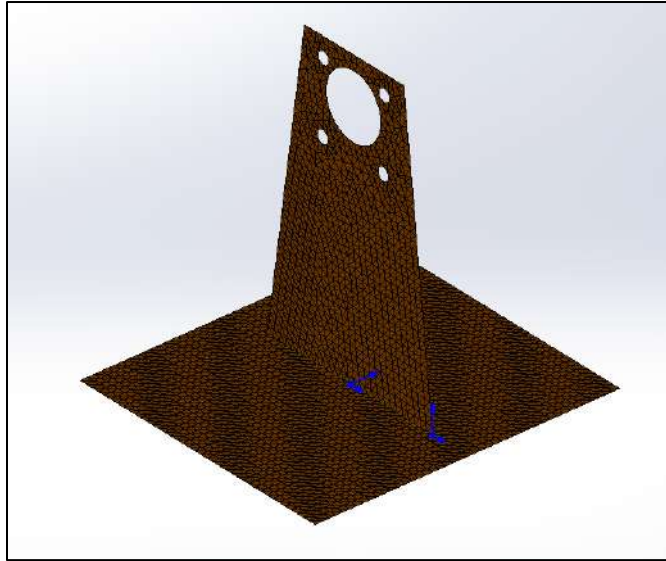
Mallado del elemento a ser simulado para análisis de soldadura.
